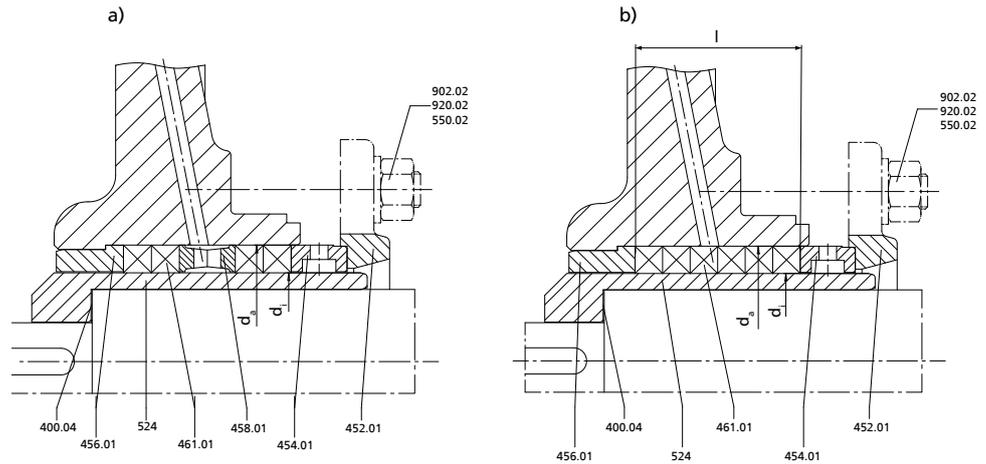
Монтаж набивочной камеры сальника а) с блокировочным кольцом и б) без блокировочного кольца
